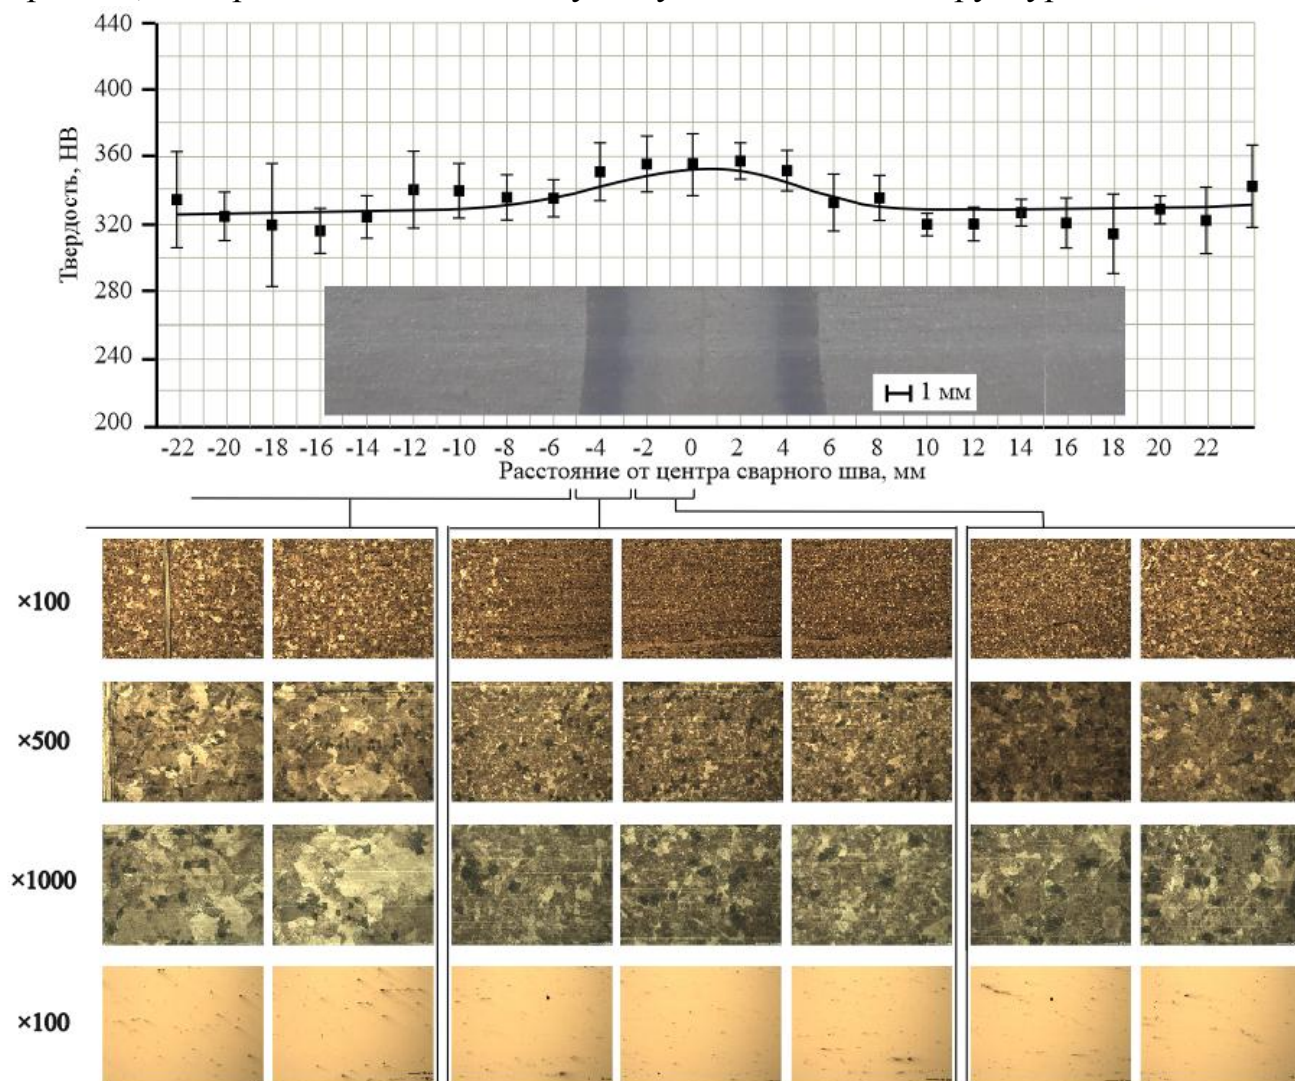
Распределение твердости, неметаллических включений и структуры в сварном соединении образца № 4
